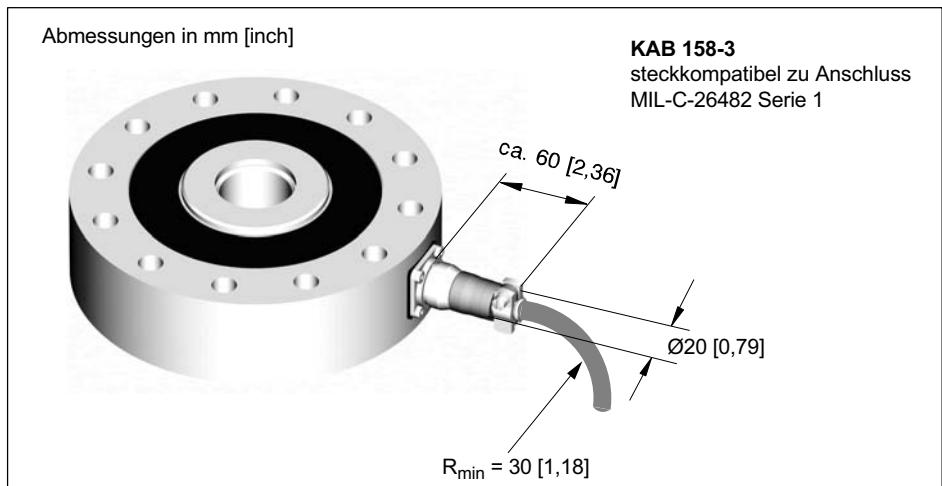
Einbauraum für Anschlussstecker mit
